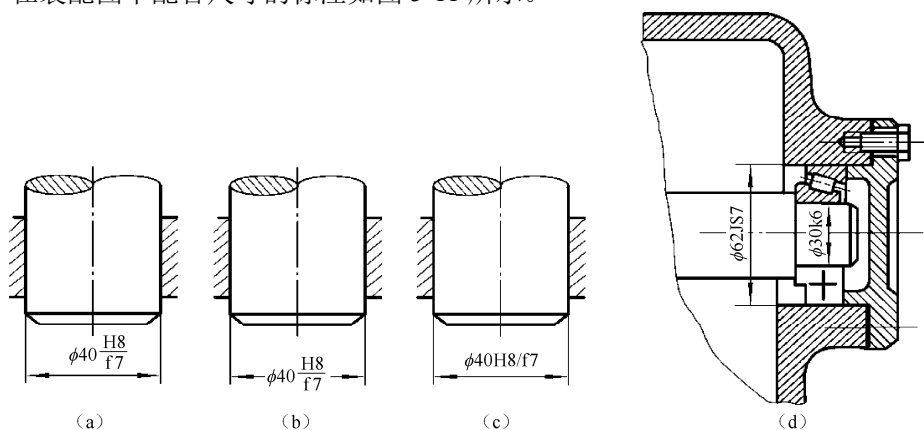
尺寸公差与配合在装配图中的标注实例
